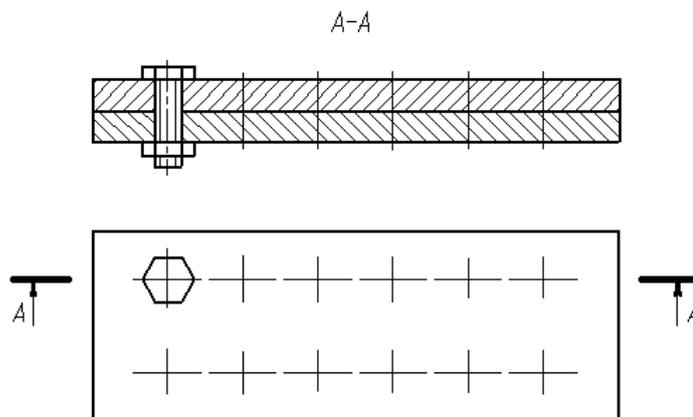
Изображение на сборочном чертеже ряда однотипных соединений
